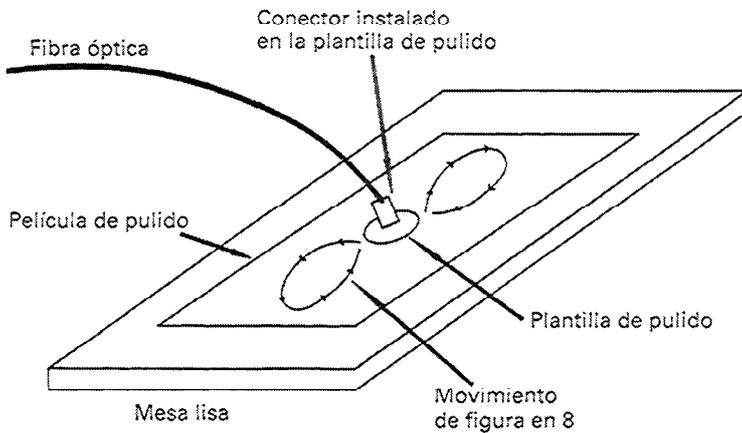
Sistema de pulido de un conector instalable en campo.
